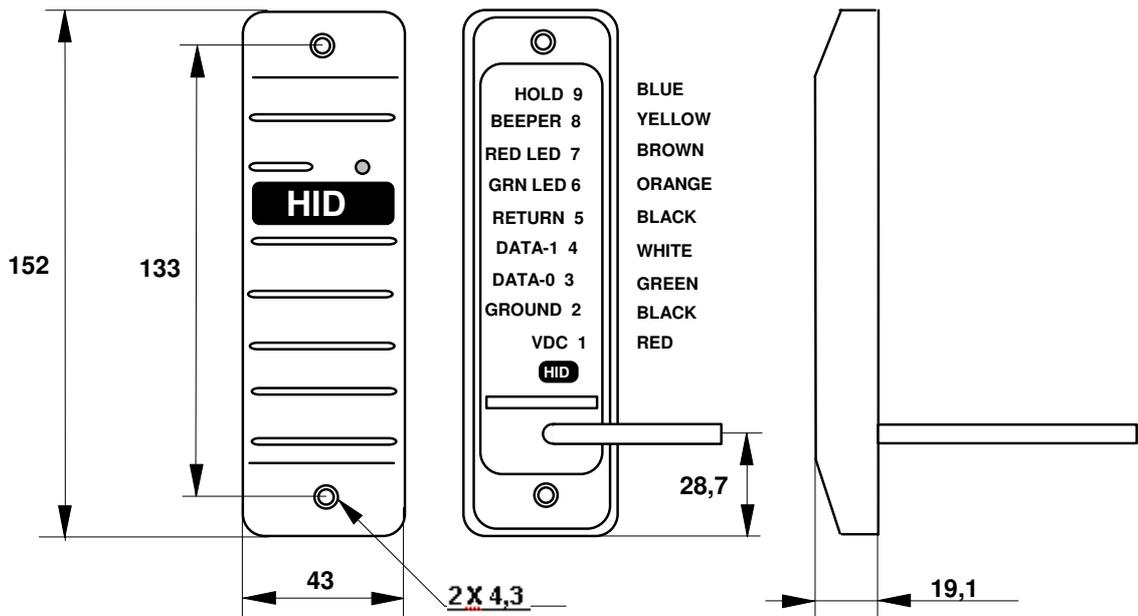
Внешний вид и габаритные размеры (в мм) считывателя MiniProx
